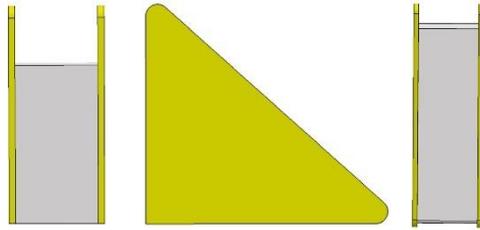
ALZADO Y PERFILES DEL MÓDULO ARMARIO
